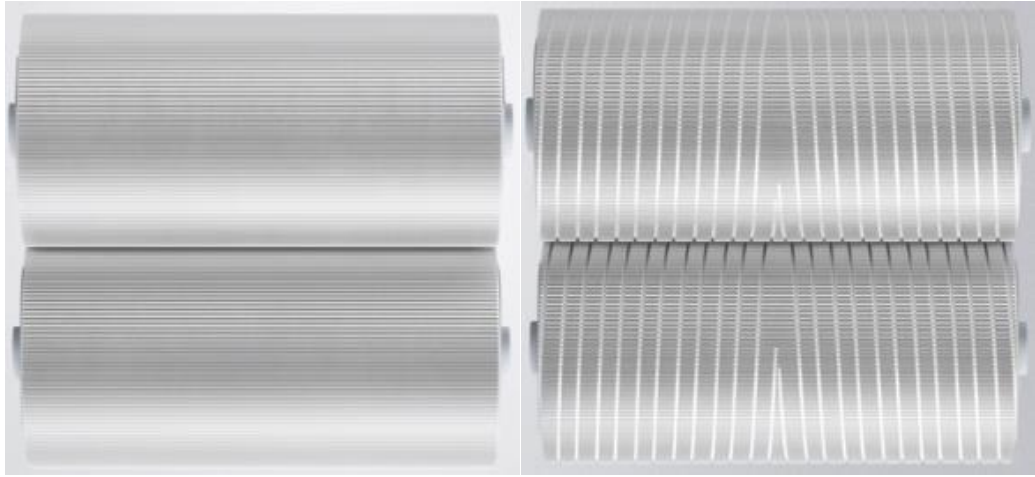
Вальці R–Cracker та RS–Cracker дробарки
